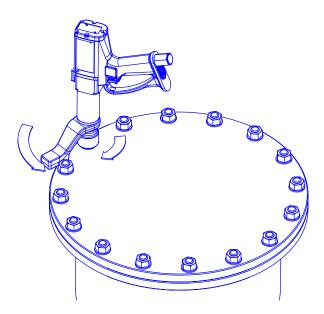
Befestigungselemente mit Rechtsgewinde festziehen
